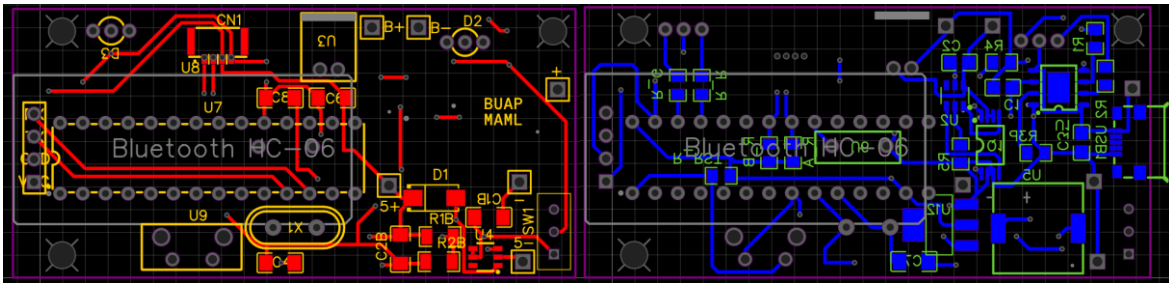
Diseño de la tarjeta PCB. a) Capa superior b) Capa inferior.
